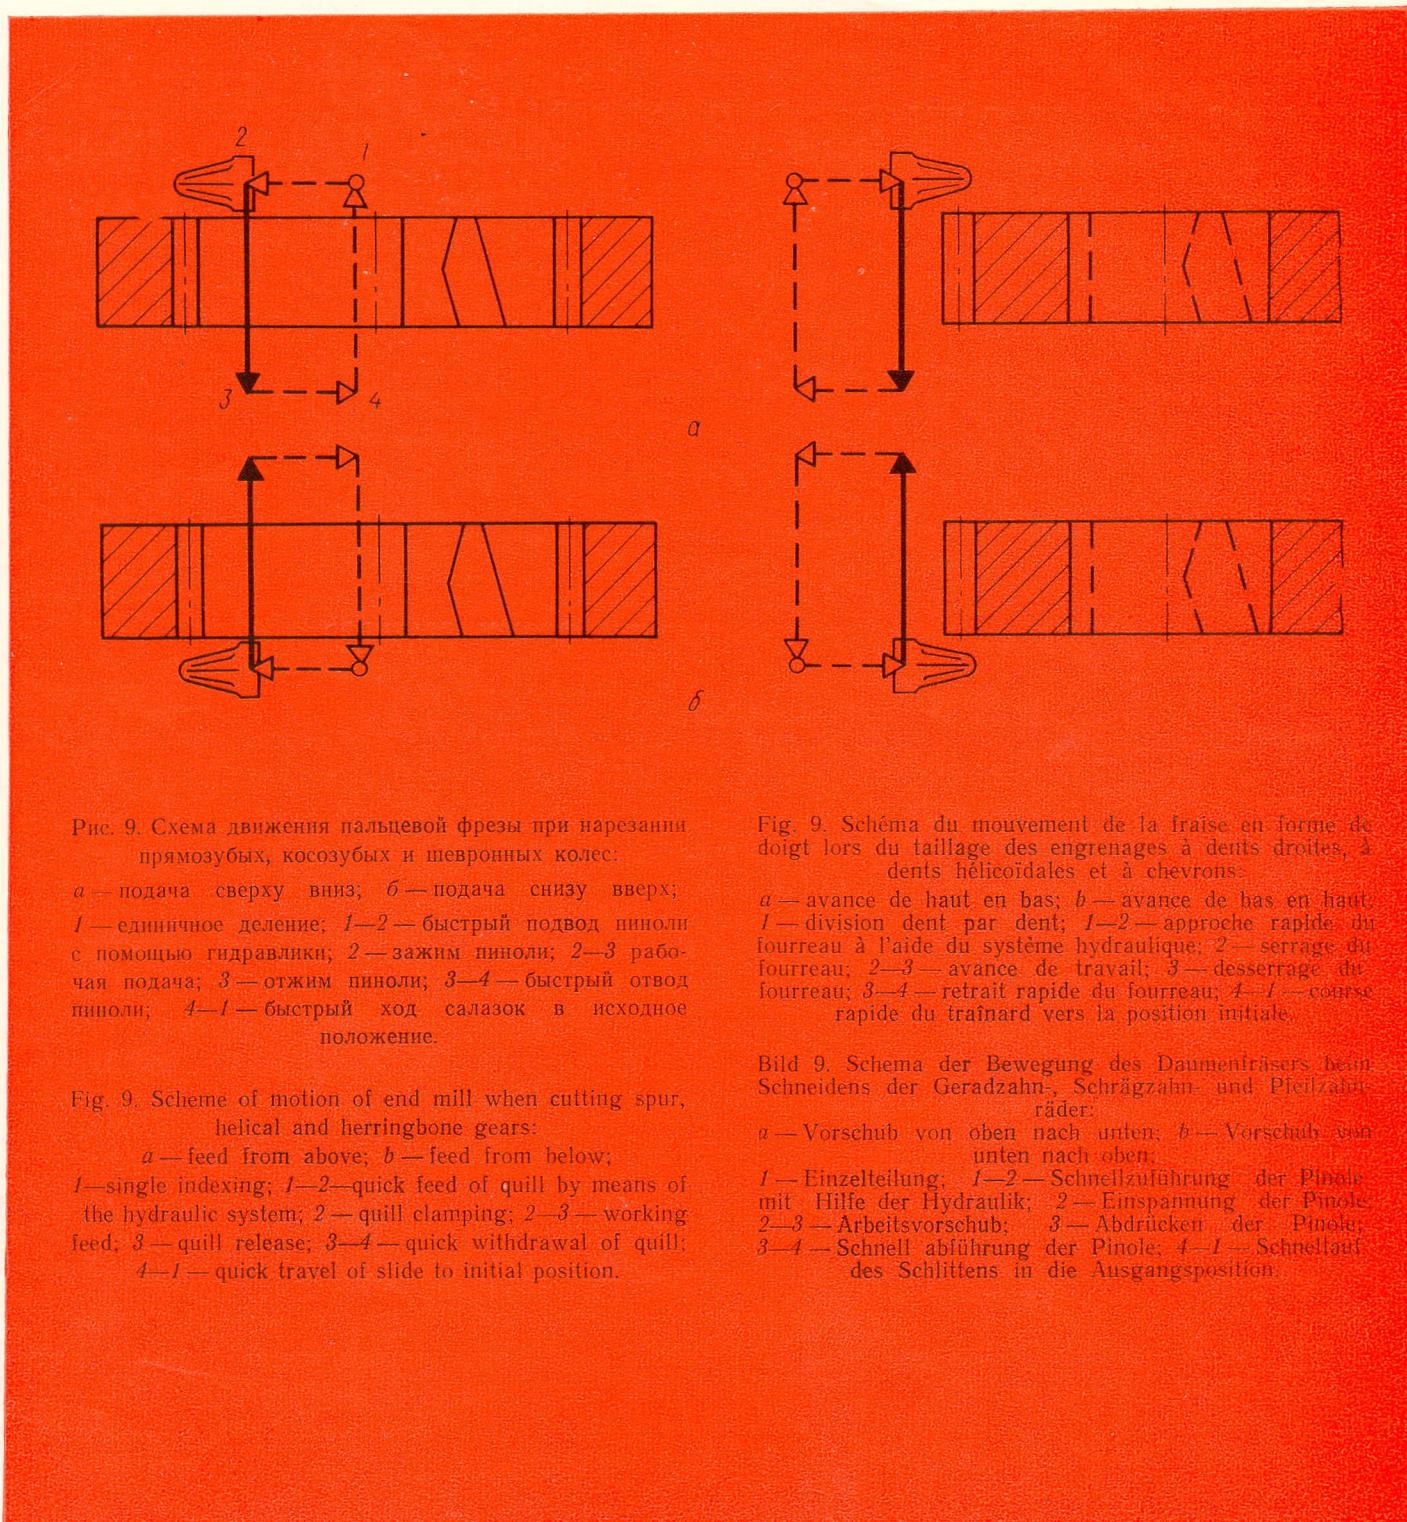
Схема движения пальцевой фрезы при нарезании прямозубых, косозубых и шевронных колес:
